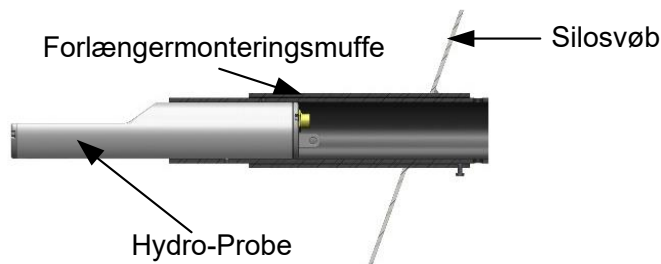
Hydro-Probe installeret i en forlængermonteringsmuffe
